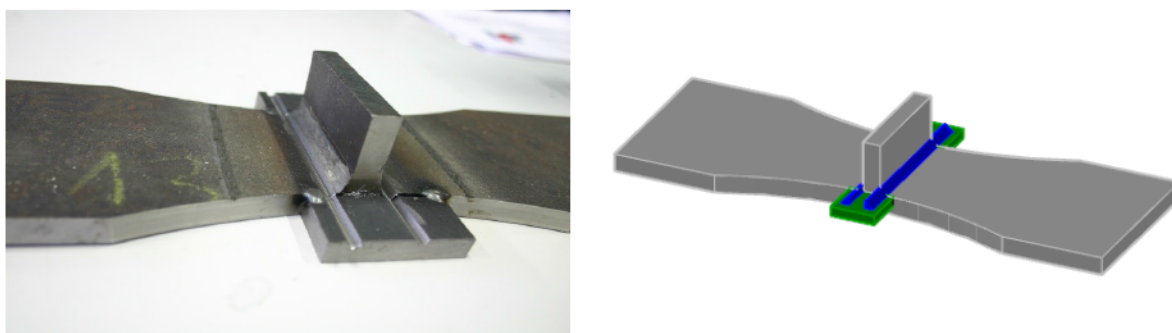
Auslaufbleche während des Reparaturschweißens
